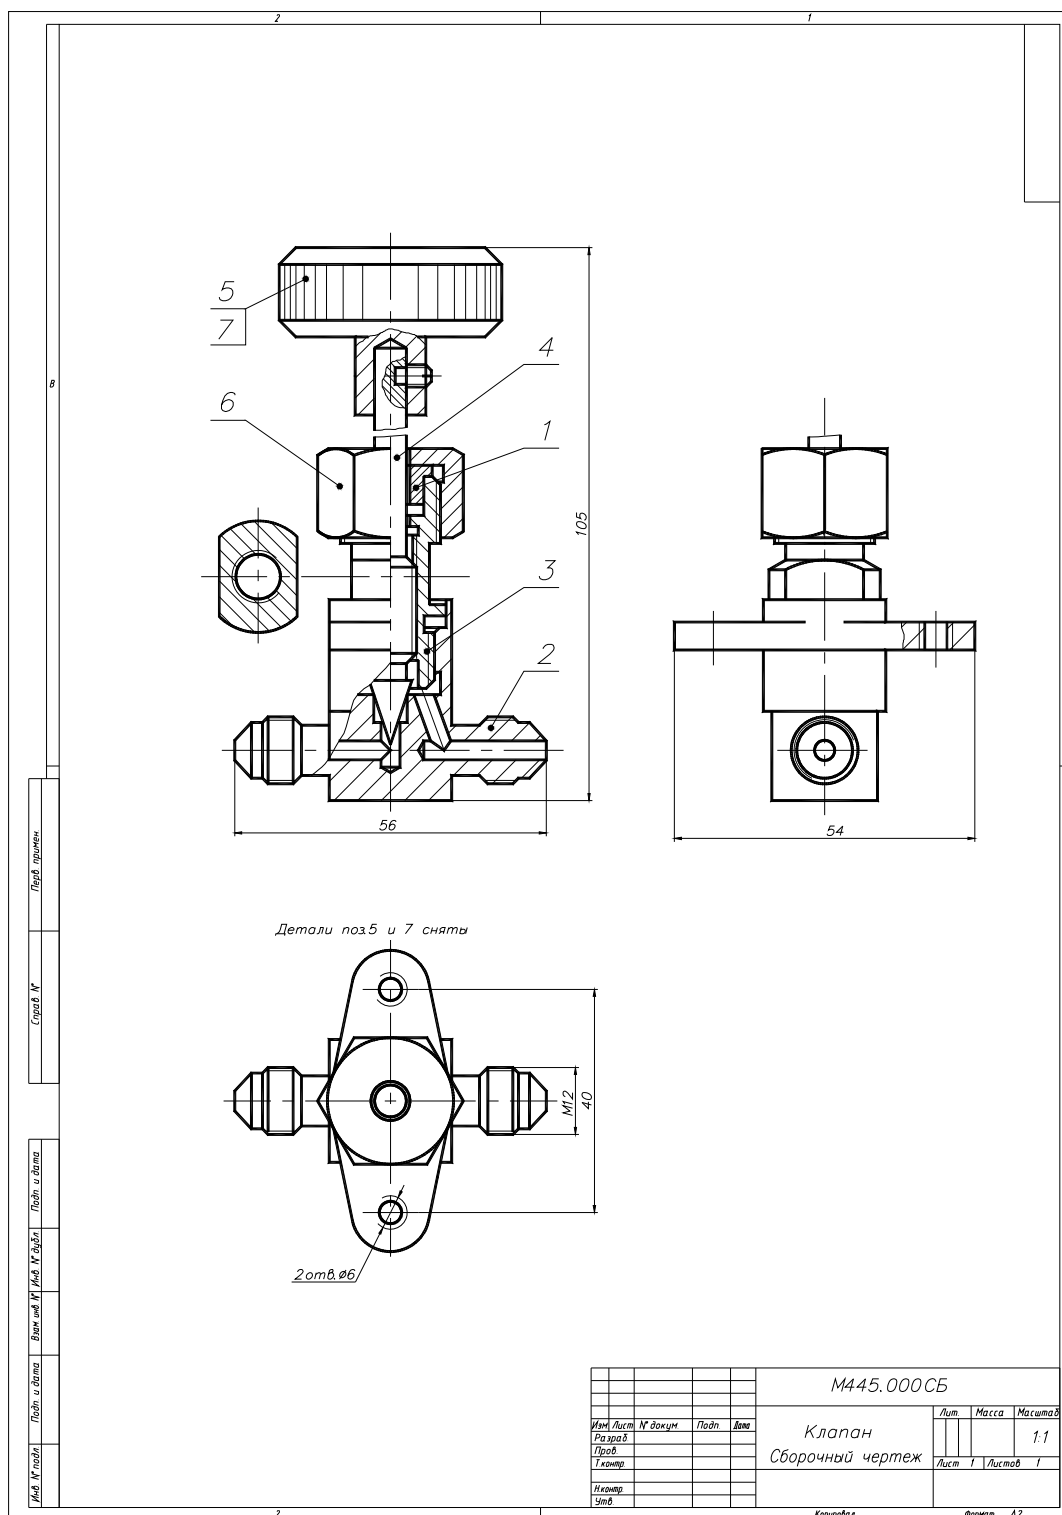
Сборочный чертеж детали «Клапан M445.000 CB».
